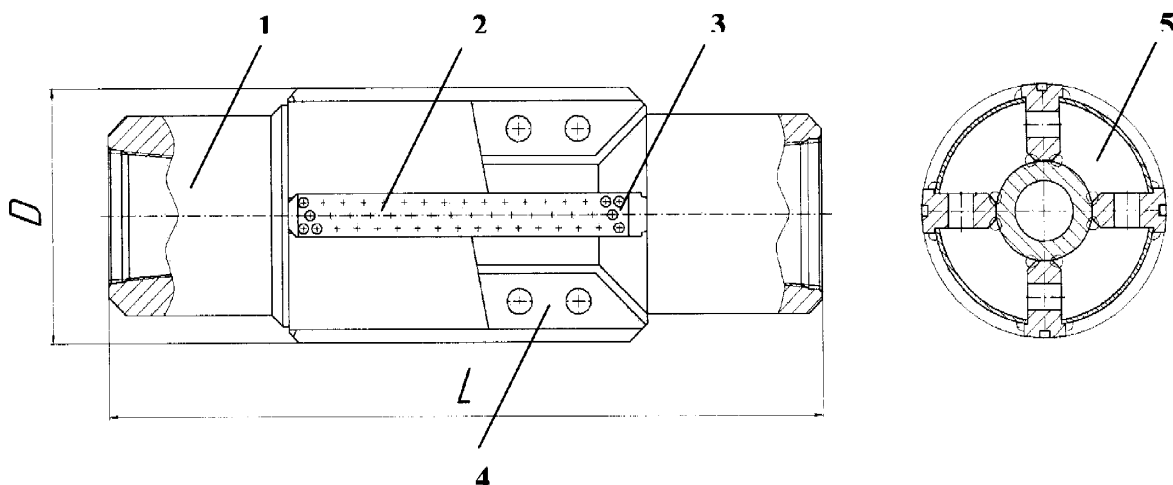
Конструктивна схема металоуловлювача-калібратора ІНМ-МУК-212,7.
